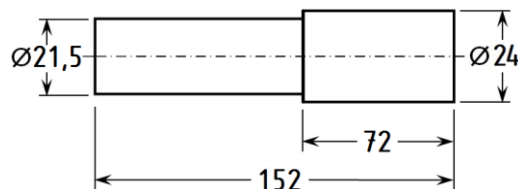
Vista do corpo de prova pré-usinado (cotas em mm)
